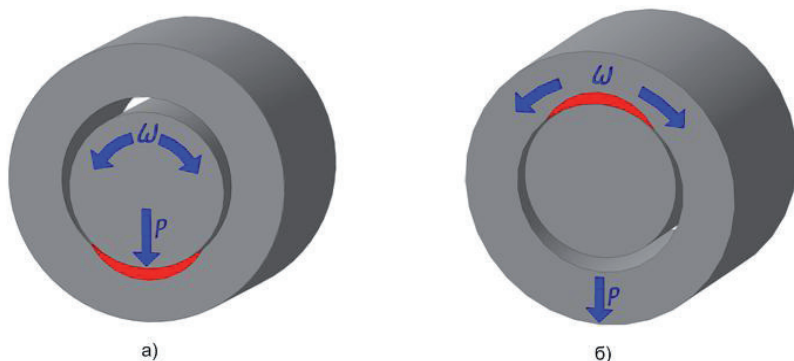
Контактное взаимодействие деталей гладких цилиндрических сопряжений: а) опорное отверстие и подвижный вал; б) опорный вал и подвижное отверстие
